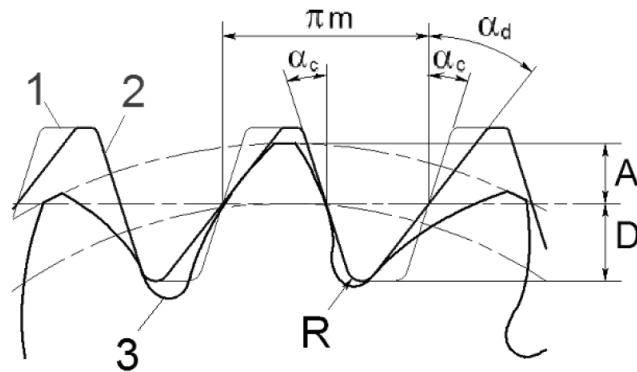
Асиметричний початковий контур черв'ячної фрези для формування евольвентного асиметричного профілю
